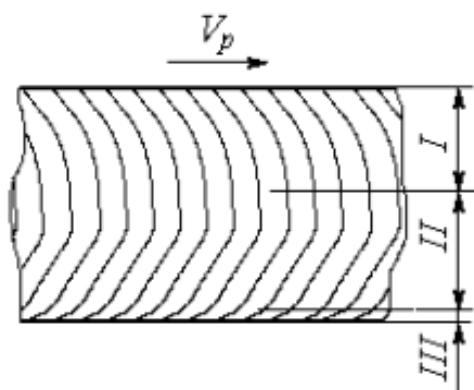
Схема расположения борозд на поверхности реза в углеродистой стали
